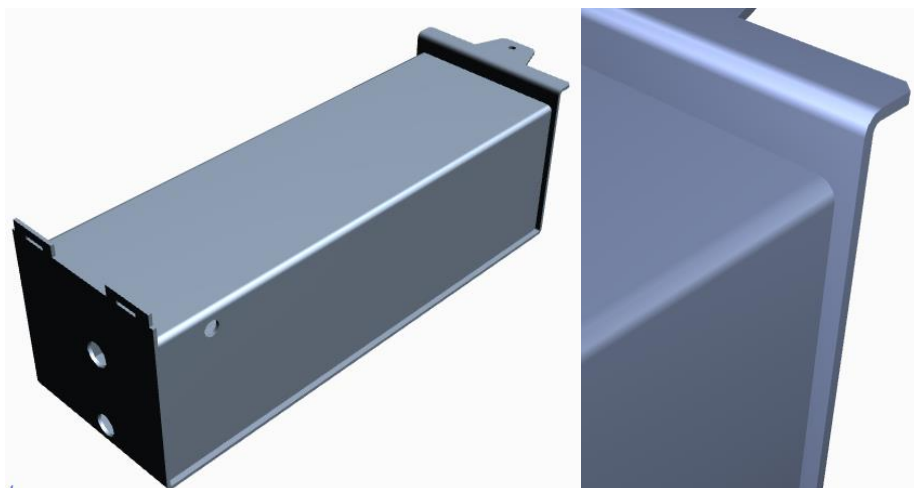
Vnitřní plášť kotlového tělesa a detail upraveného otvoru.
